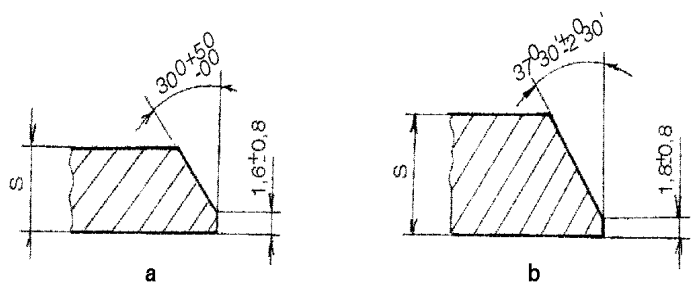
Sanfren în V cu fațetă frontală executată mecanic: a- frecvent; b- opțional ($S \leq 22$ mm).
